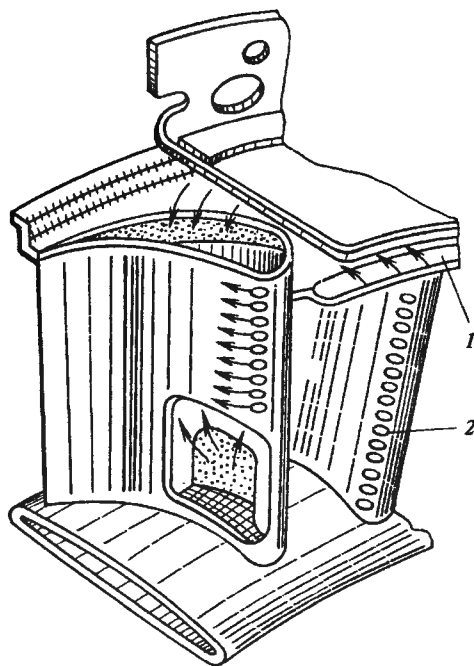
Схема охлаждаемой воздухом направляющей лопатки
